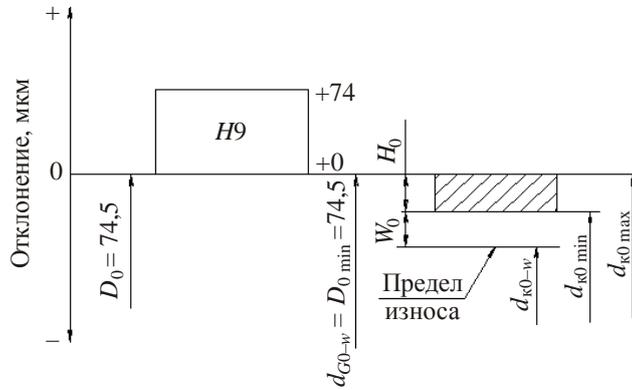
Схема расположения поля допуска калибра с базовым измерительным элементом:
